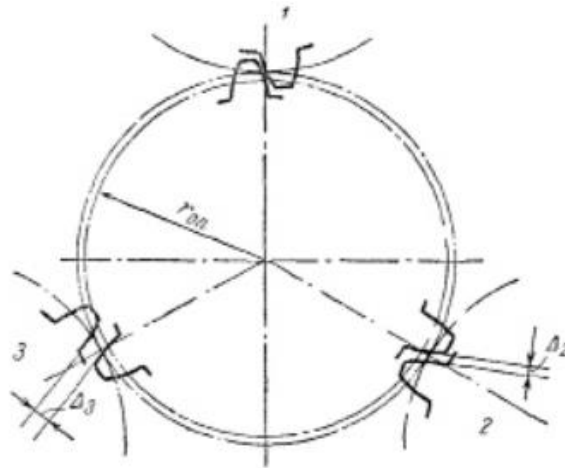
Схематичное изображение контакта зацепления трехсателлитной планетарной передачи
